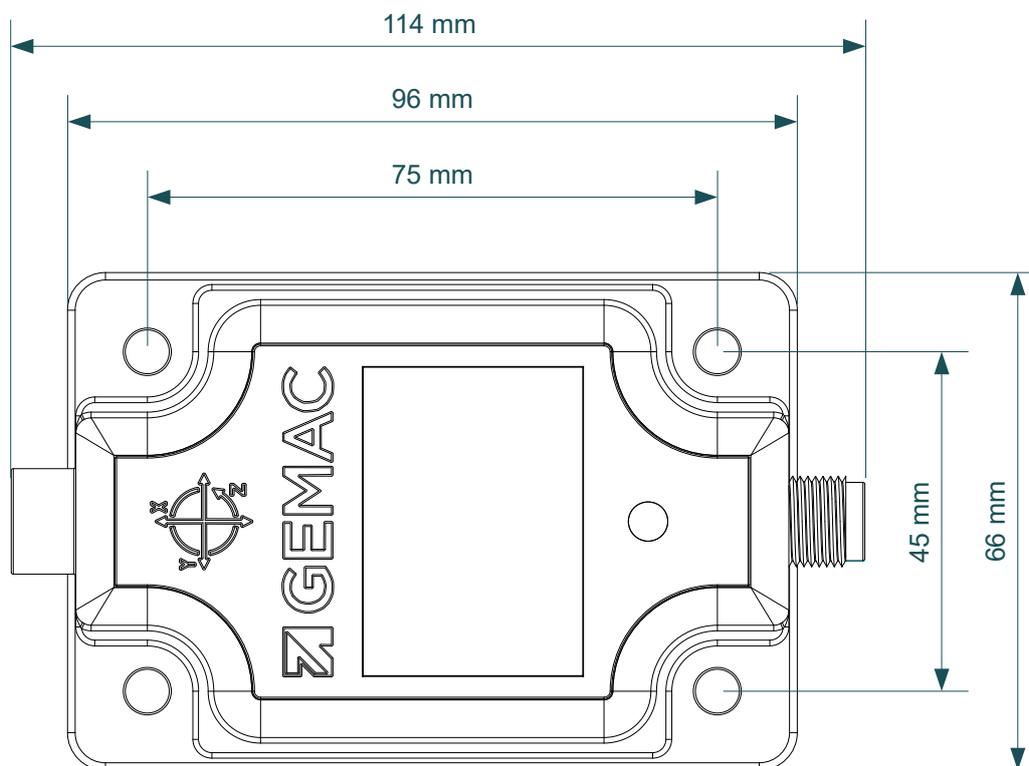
Befestigungsbohrungen (Maße in mm)
